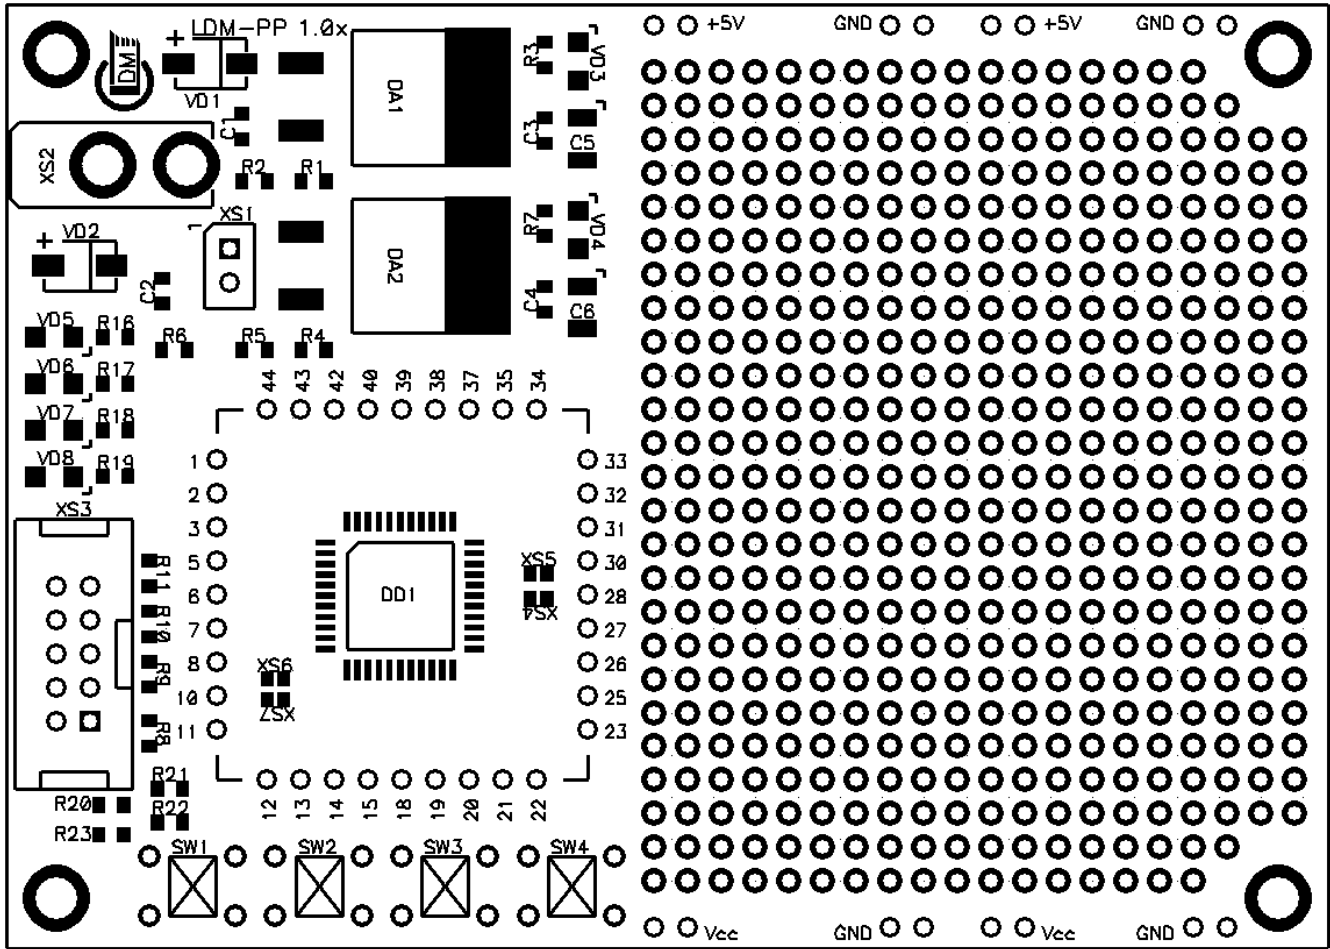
Внешний вид печатной платы конструктора-ПЛИС LDM-PP 1.xxxx
